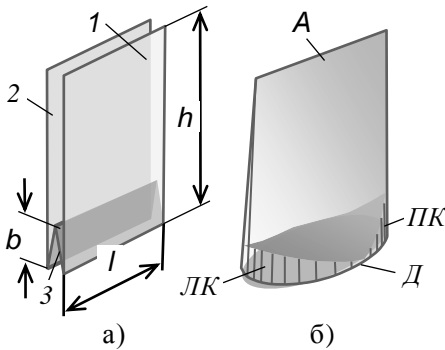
Пакування з гнучкого матеріалу: конструкція заготовки (а); форма засобу пакування (б)
